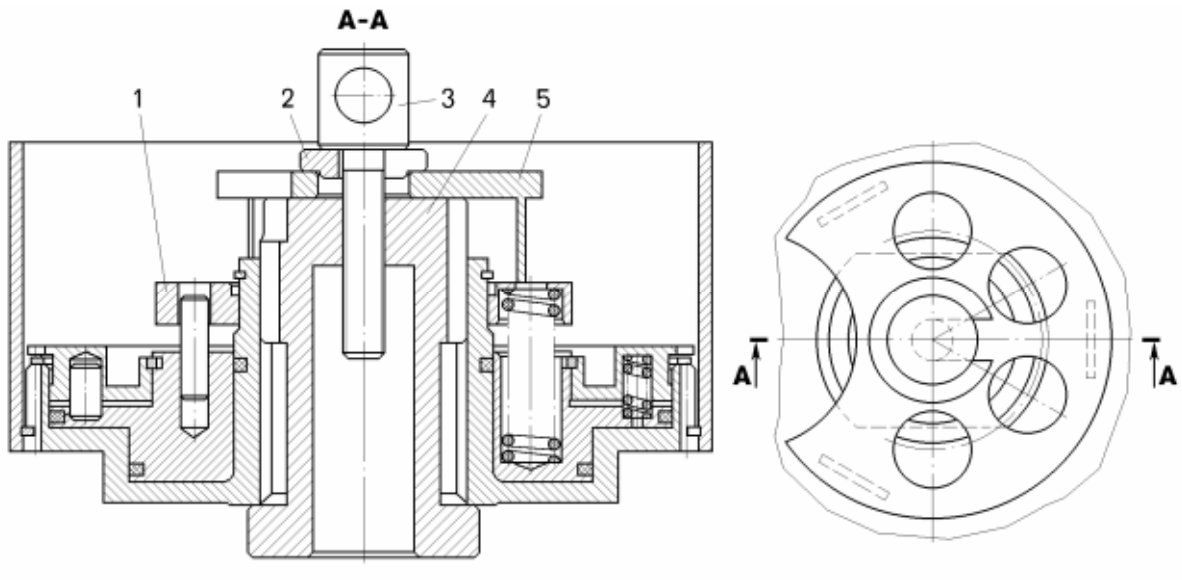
Приспособление для сборки и разборки фрикционов:
